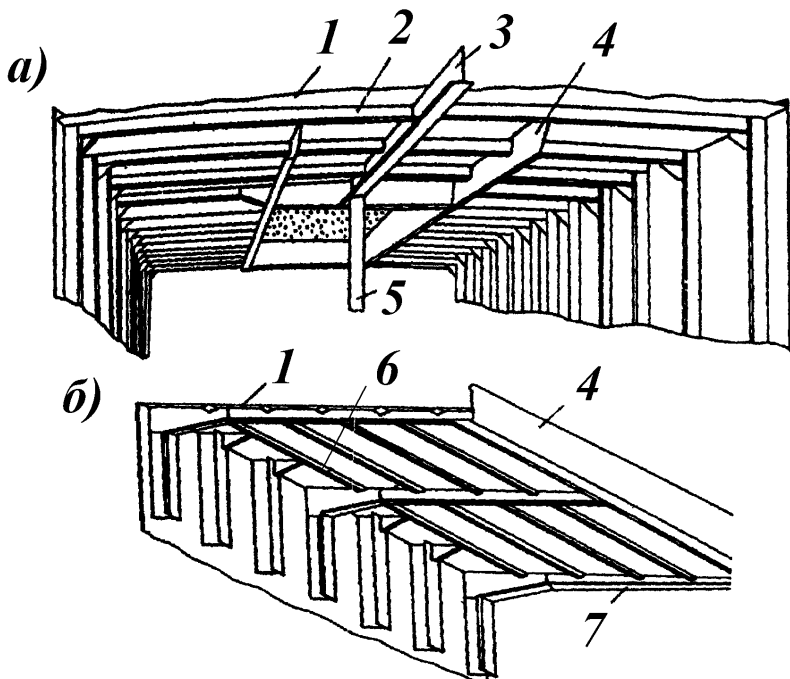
Конструкция палубных перекрытий: *а* – поперечная система набора, *б* – продольная система набора; 1 – палуба, 2 – бимс, 3 – карлингс, 4 – комингс, 5 – пиллерс
